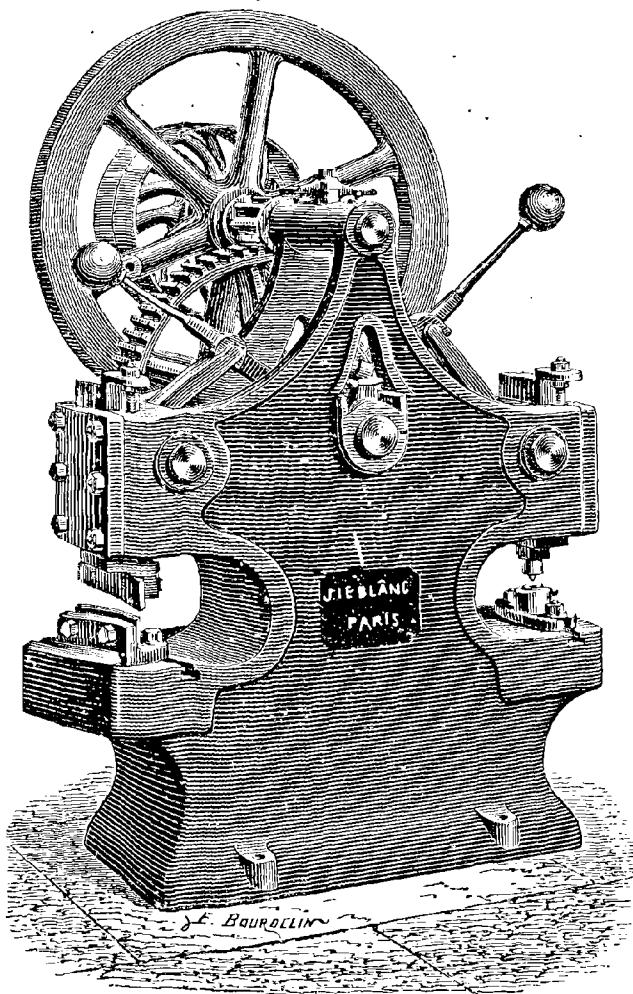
Cisaille-poinçonneuse à deux faces de M. Le Blanc.
